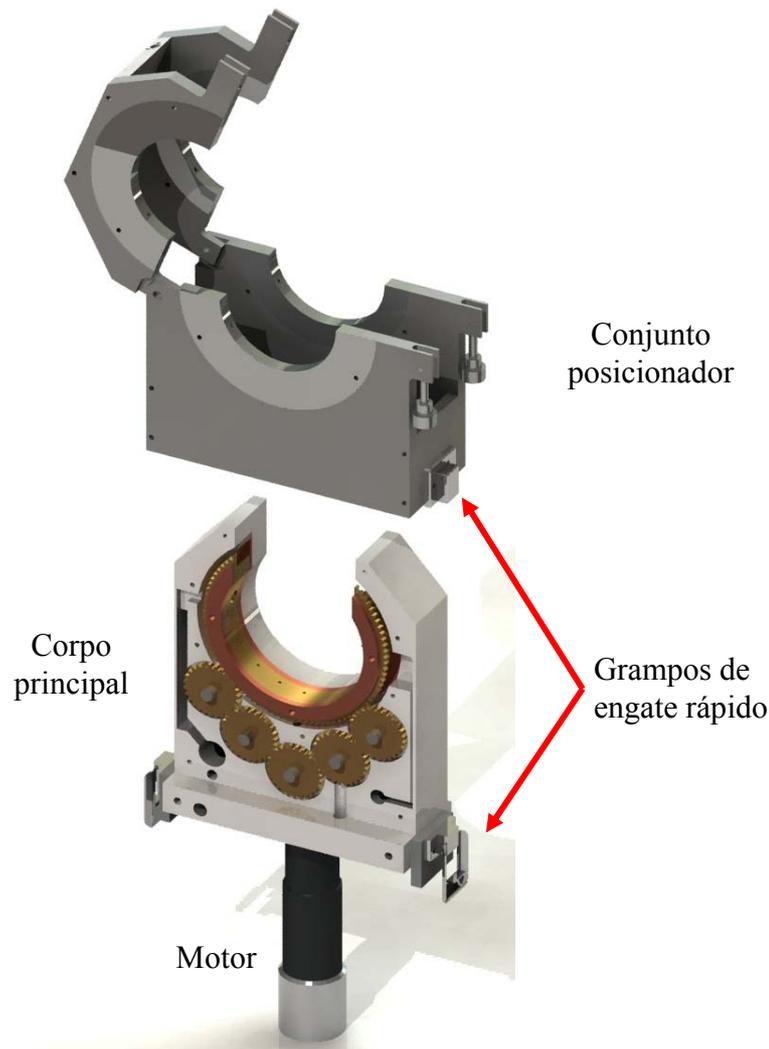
Corpo principal do cabeçote orbital montado e acoplamento do conjunto posicionador
